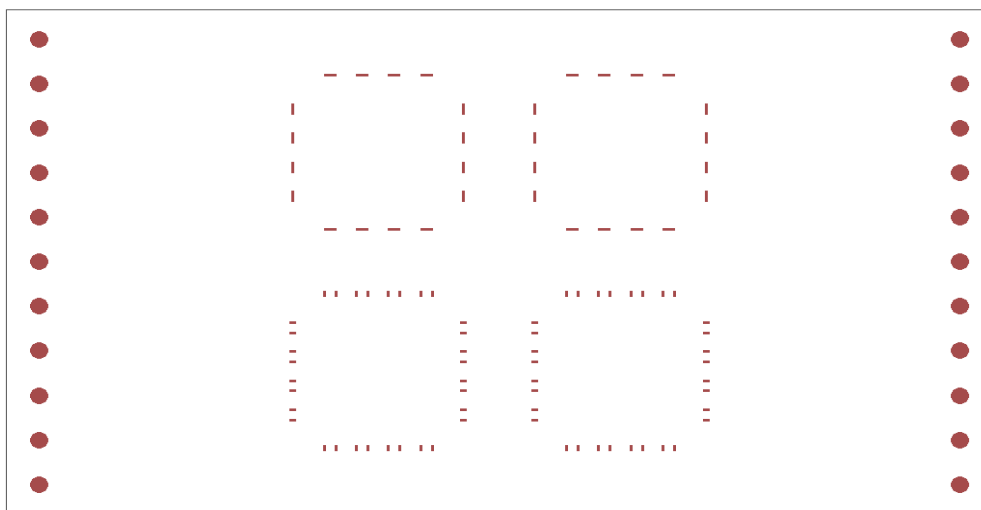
Layout testovací desky určené pro druhou část měření
